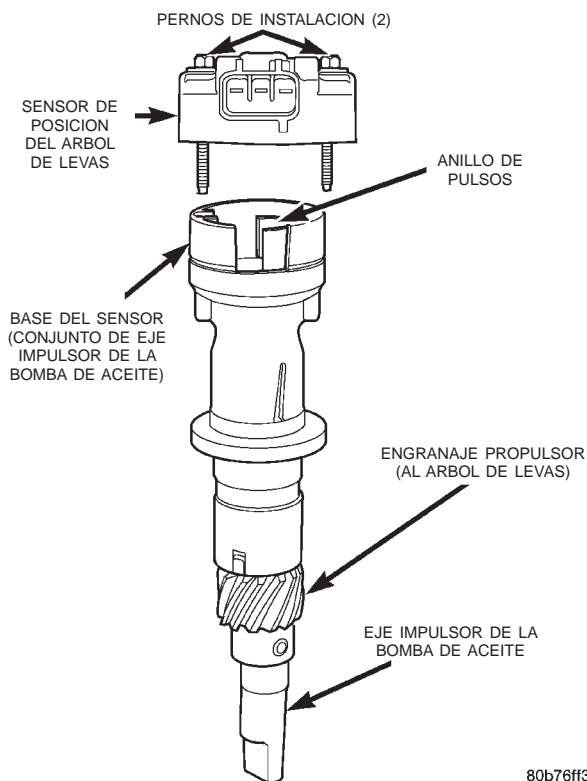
CMP y eje impulsor de la bomba de aceite—motor 4.0L
